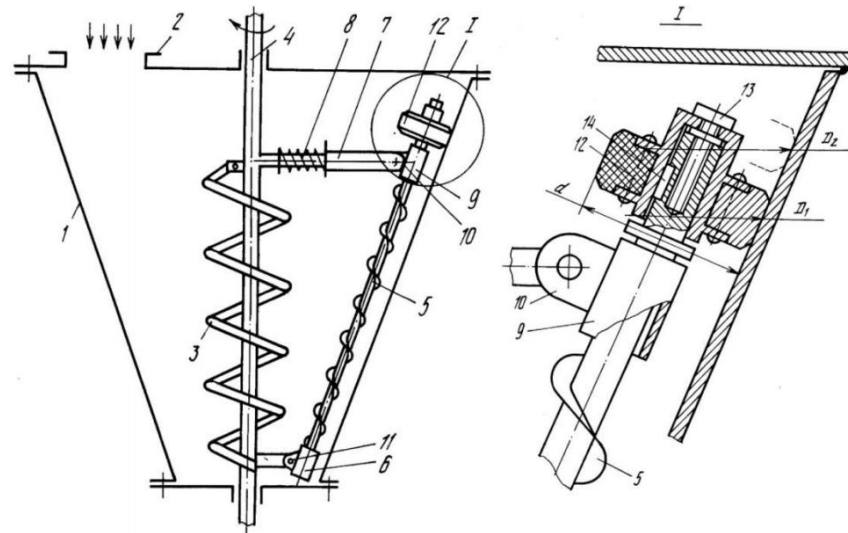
Змішувач: 1 – корпус; 2 - завантажувальний і розвантажувальний патрубок; 3 - спіральний елемент; 4 - приводний вал; 5 – шнек; 6 - опорна п'ята; 7 – водило; 8 – гайка; 9 - опорна втулка; 10, 11 - плоскі шарніри; 12 - опорне колесо; 13 – гвинт; 14 – шпонка
